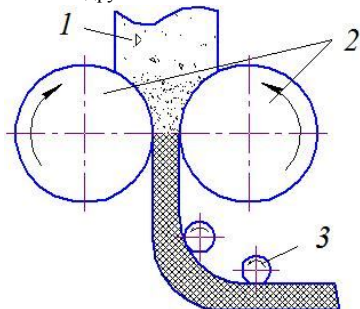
Схема прессования порошковых материалов прокаткой: 1 – емкость для порошка; 2 – вращающиеся вальки; 3 – вальки для изменения направления движения прокатанной заготовки
